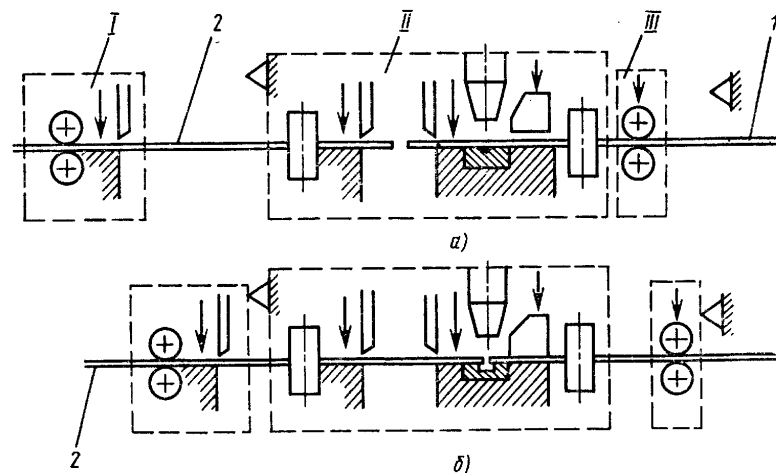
Схема «летучей» установки для сборки и сварки концов рулонов
